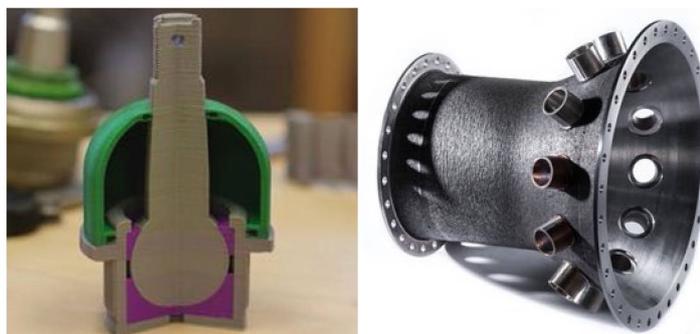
Peça em plástico multicolor e peça metálica impressas em 3D
